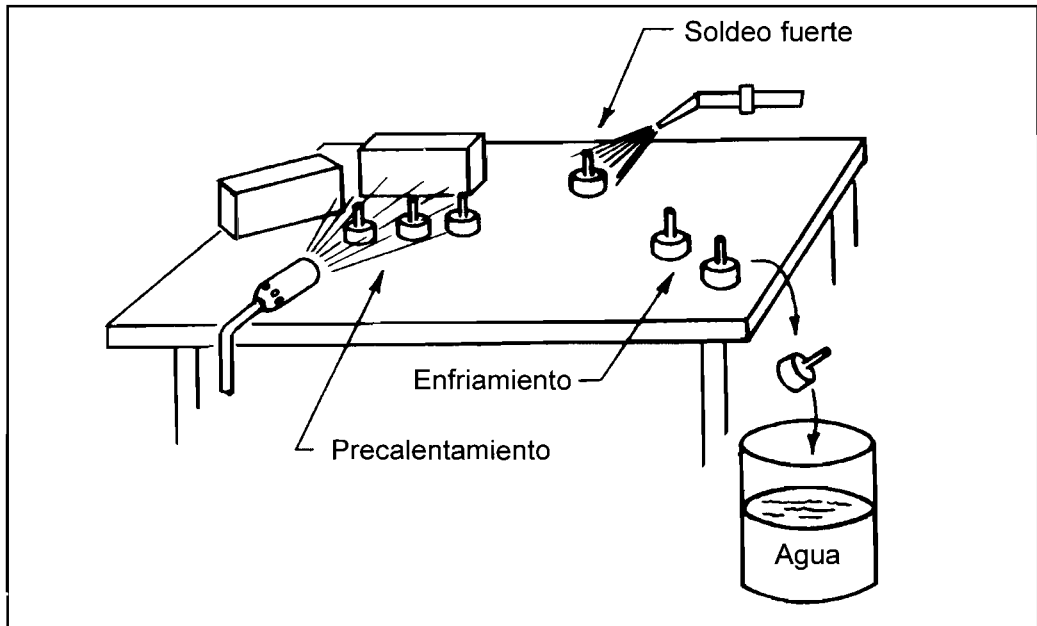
SOLDEO FUERTE DE PIEZAS PEQUEÑAS
